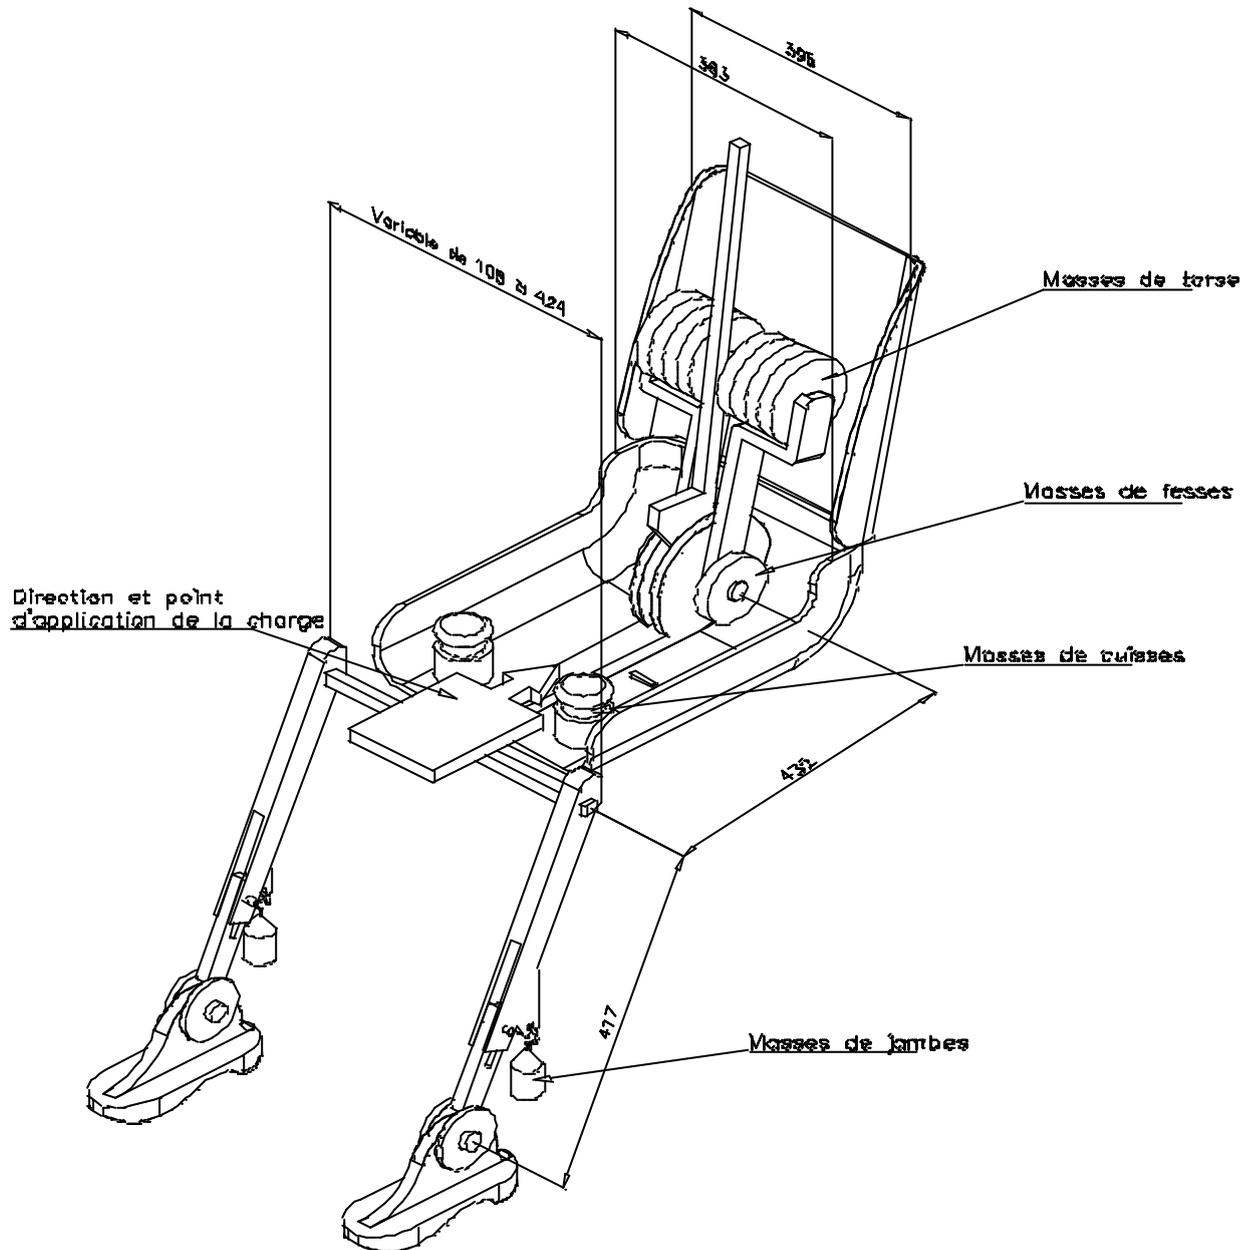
Dimensions des éléments de la machine 3 DH et emplacement des masses
